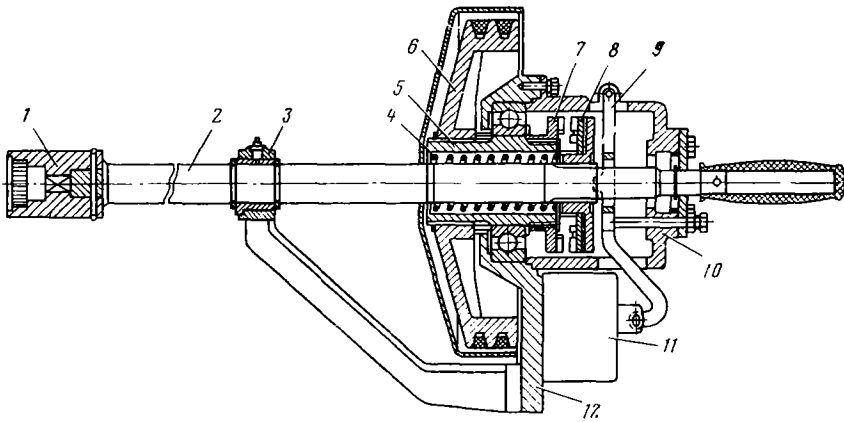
Схема ударного механизма гайковерта модели И-318 для гаек колес
